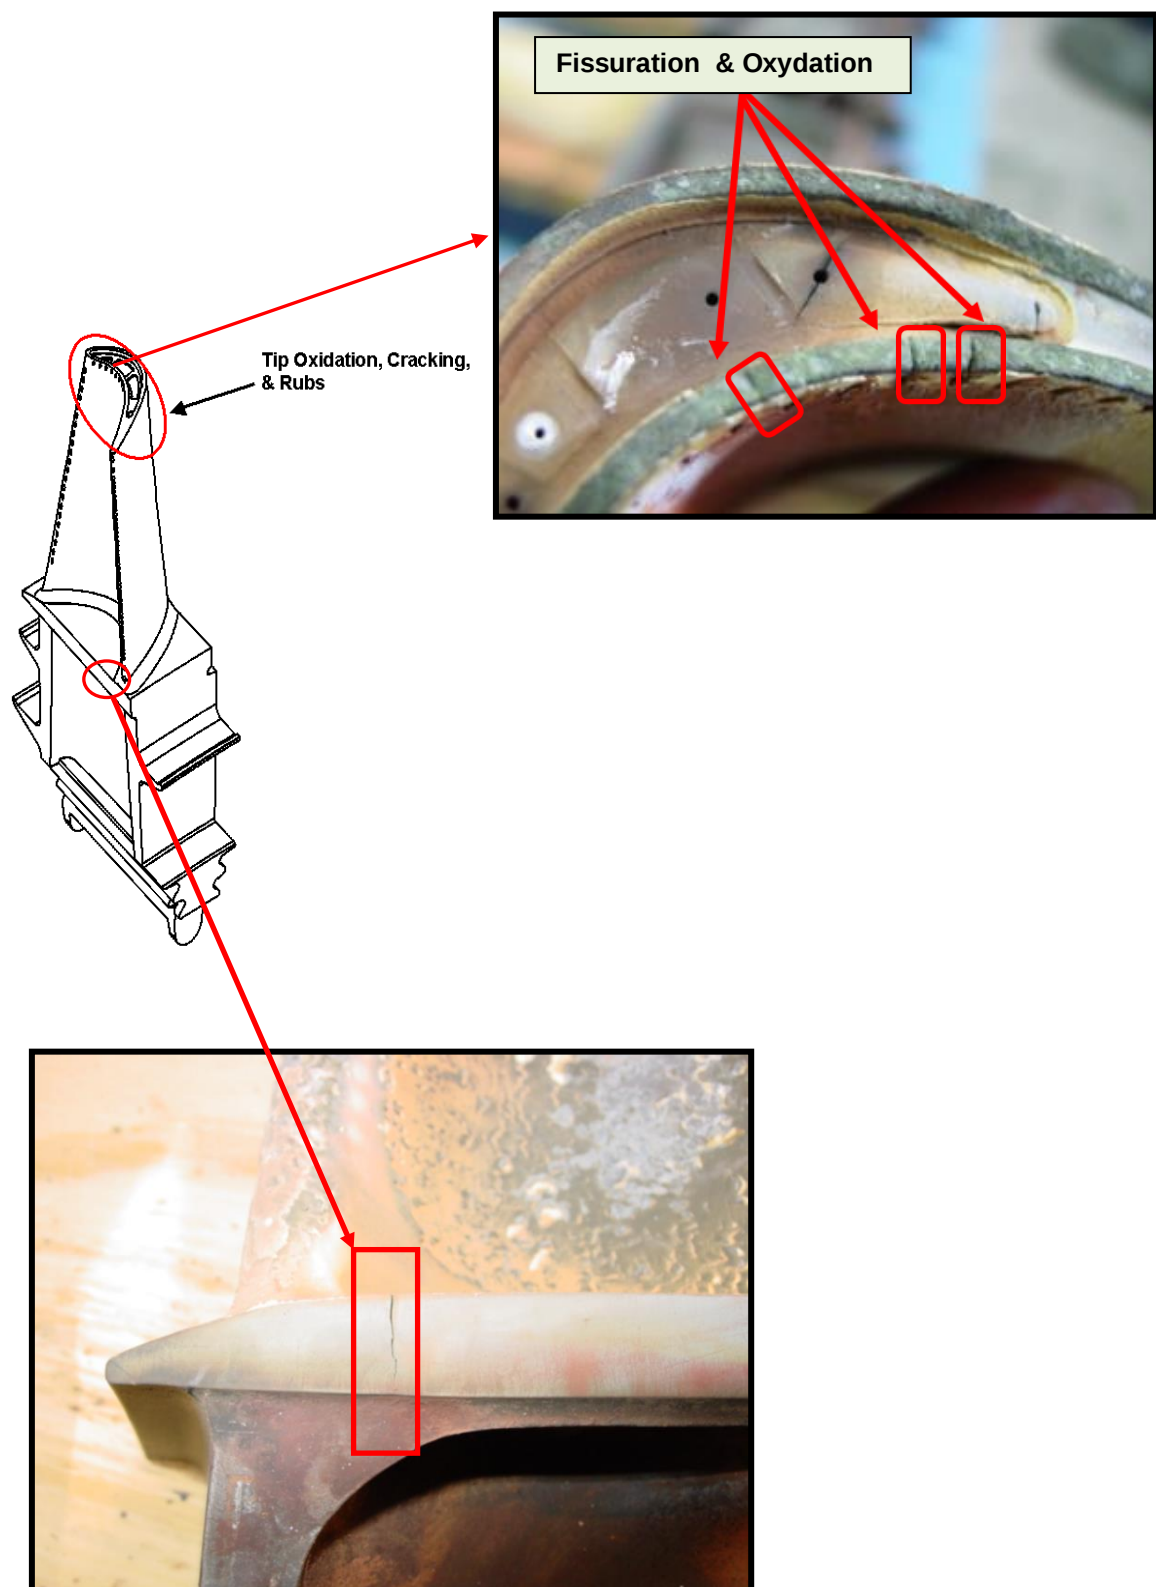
Fissuration et oxidation sur un aube de turbine a gaz
